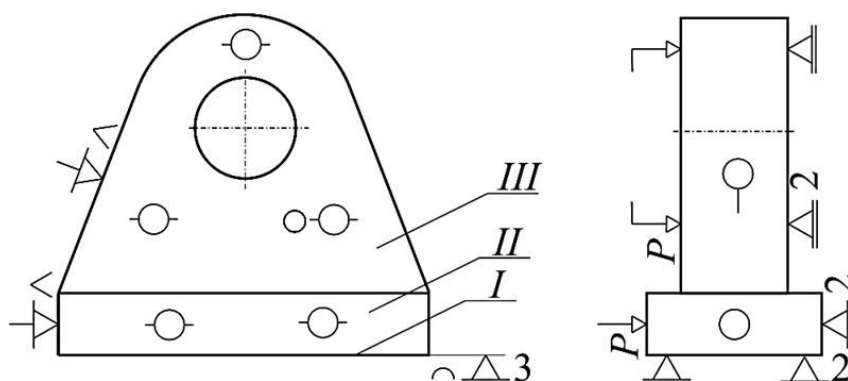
Принципиальная схема приспособления для сборки проушины
